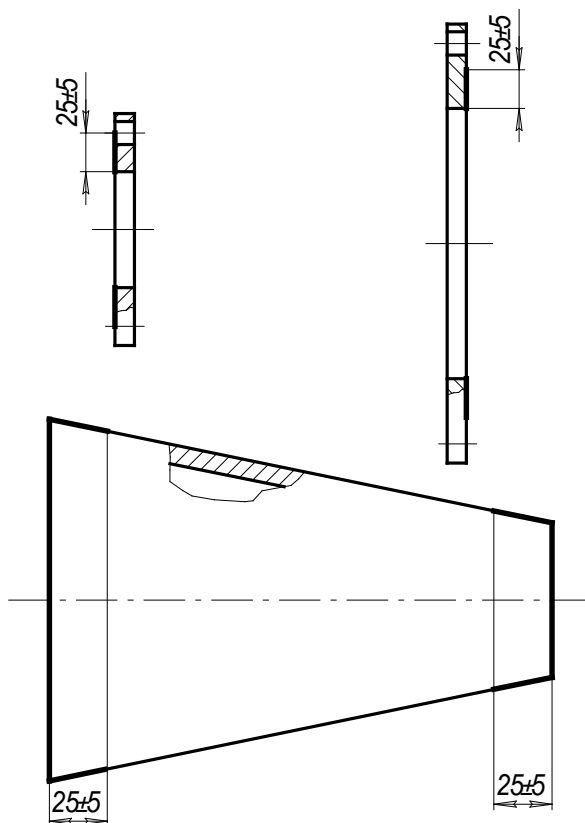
Схема зачистки заготовок под сварку
